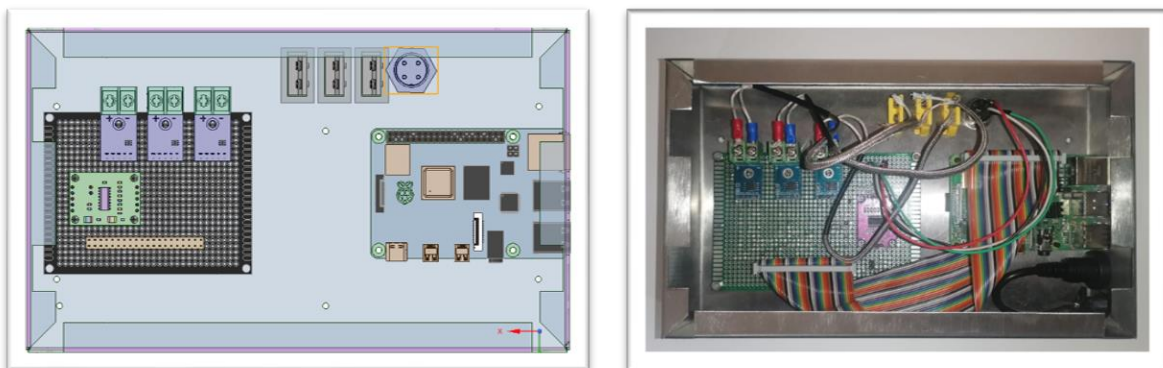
Diseño y ensamble de la caja del módulo con componentes
